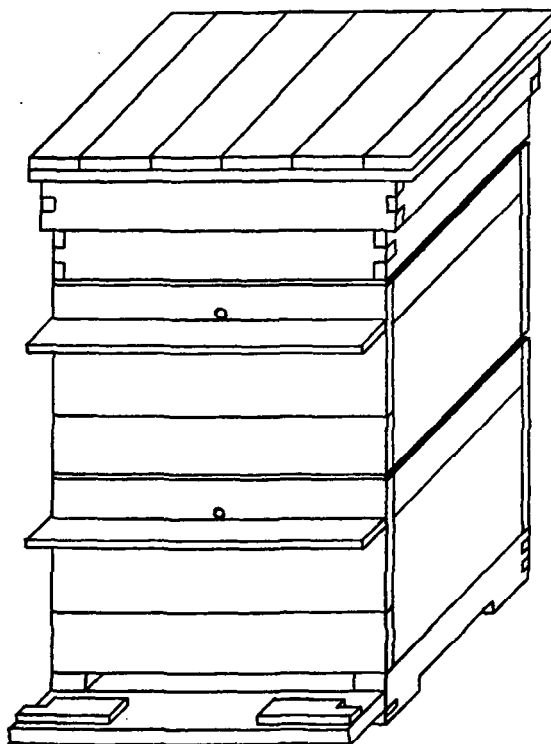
Двухкорпусный одностенный улей (общий вид)
